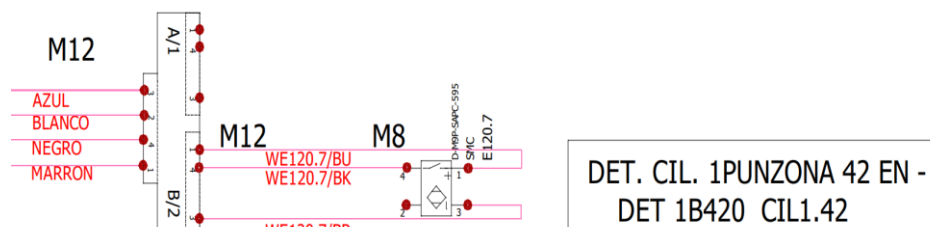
Conexiones Herramienta 42 EN – del Lado izquierdo.
